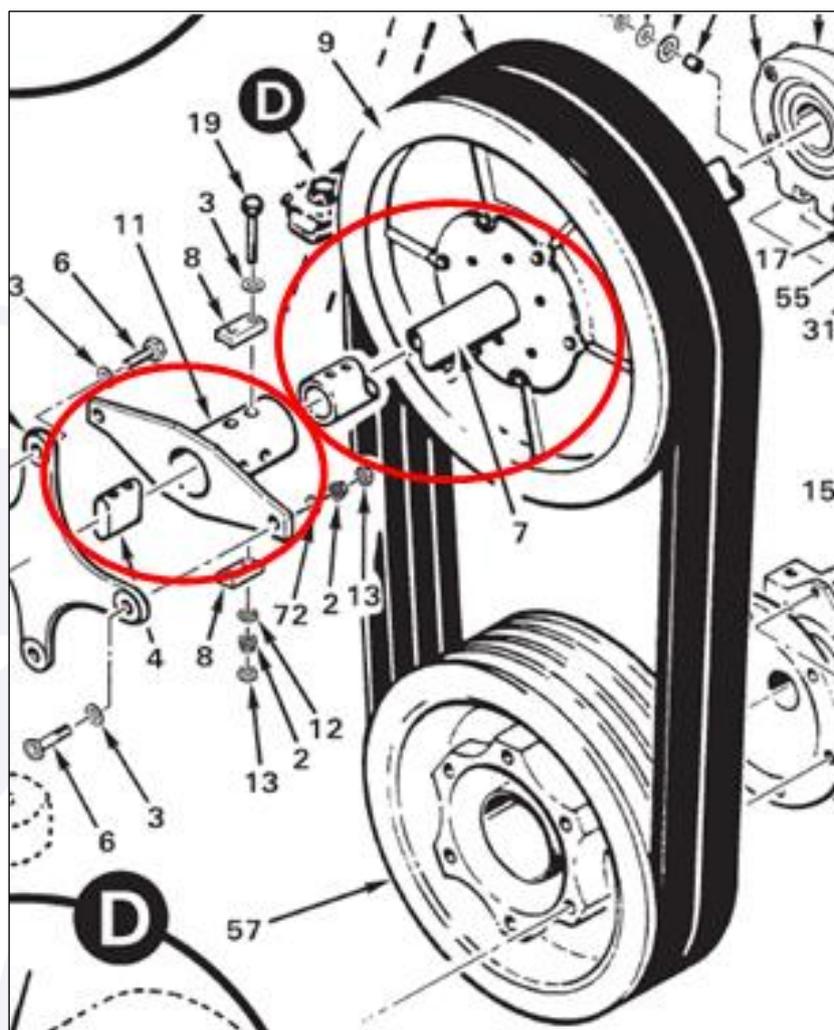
Detalhes do Yoke (11) e Shaft-Clutch (7), no Drive train do R-22
